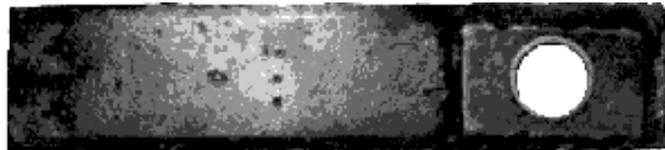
Martillo recuperado listo para la operación de recargue por soldadura.
